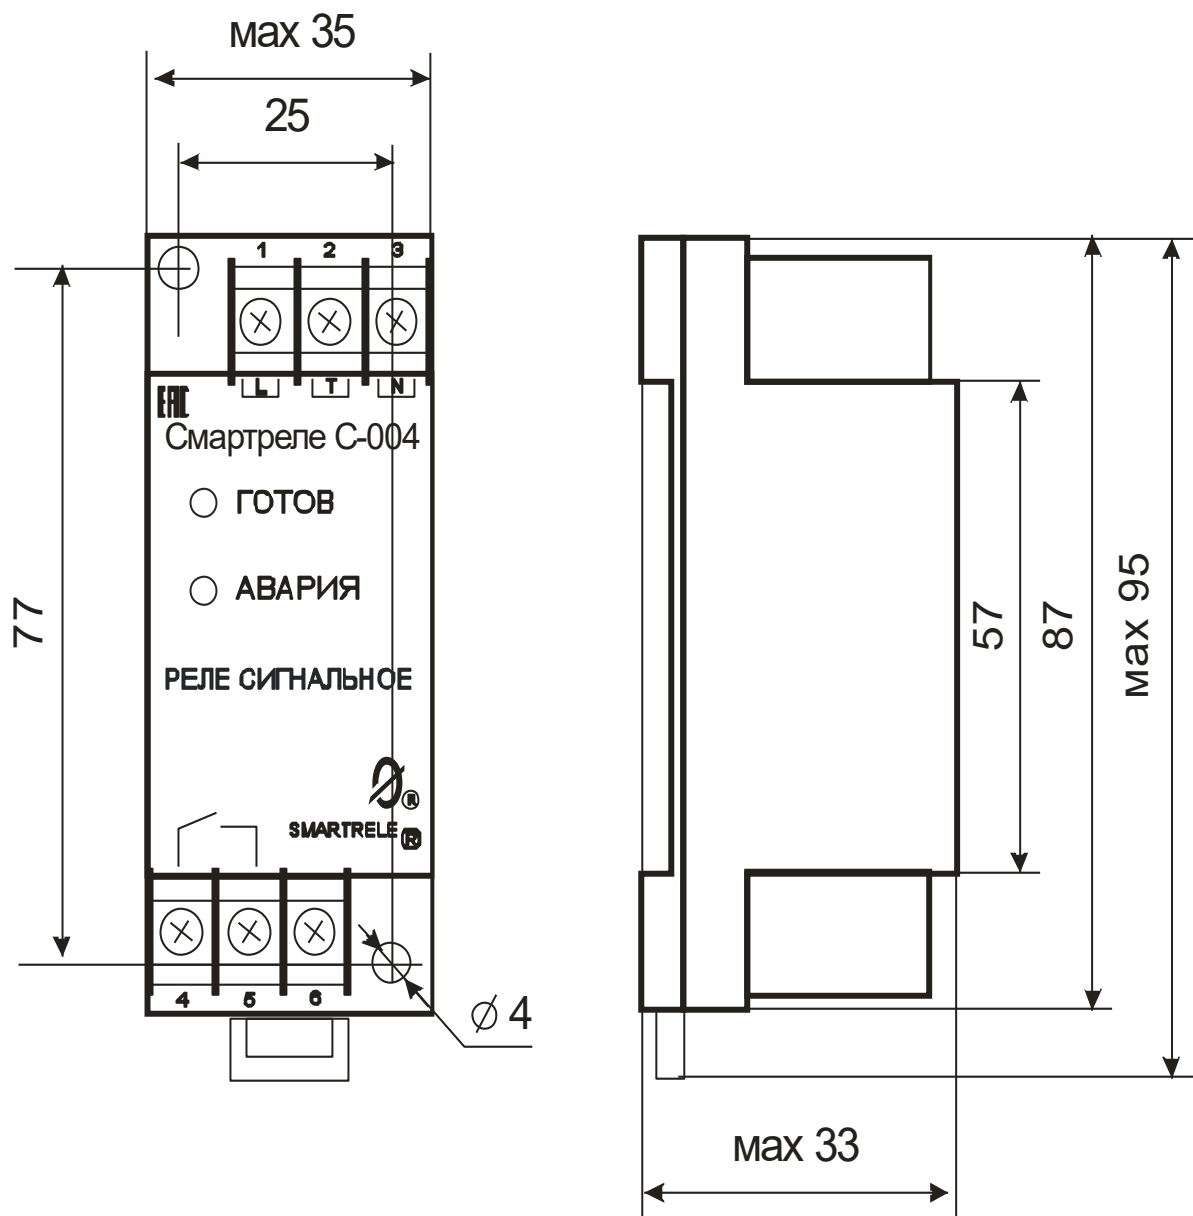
внешний вид, габаритные и установочные размеры СМАРТРЕЛЕ С-004
